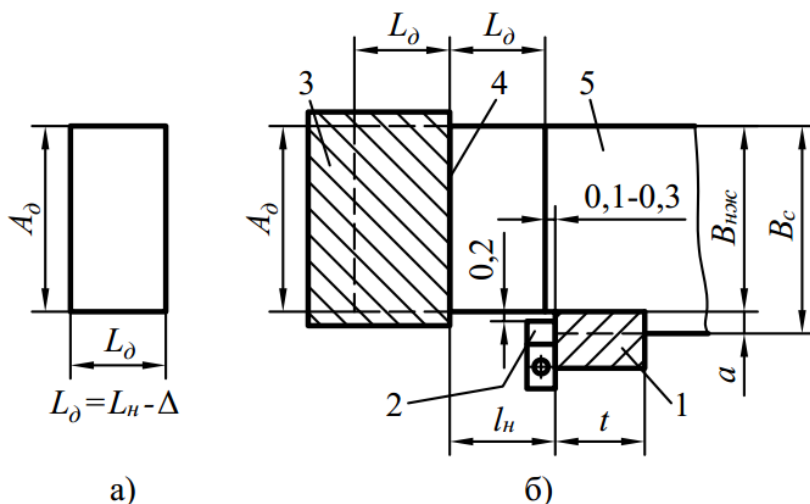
Схема відрізування заготовки без перемичок у штампі з кроковим ножом:
